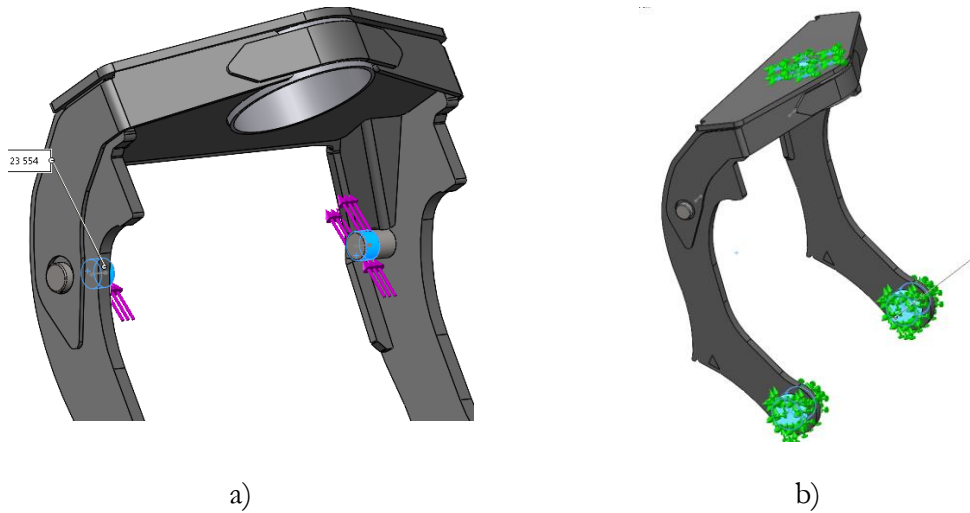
Configuração utilizada no estudo do berço: a) Aplicação de força; b) Aplicação das fixações.
